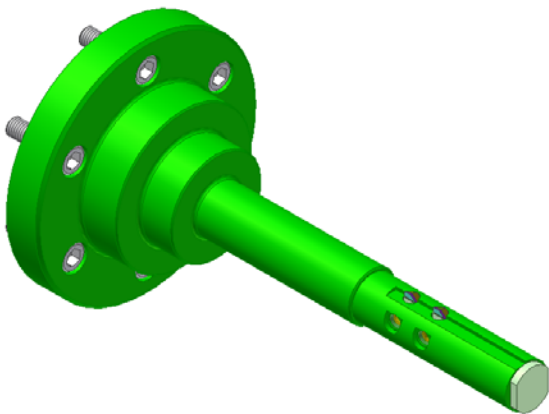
Борштанга в сборе с элементами крепления и резцом в тонированном изображении.
